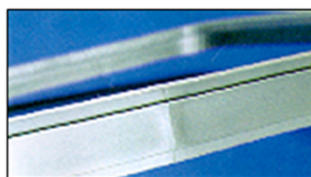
Moldeo con defecto de línea de soldadura.
